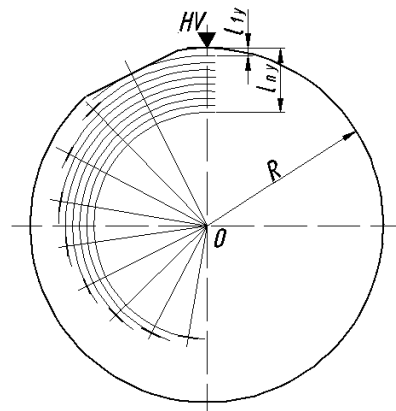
Схема розташування мікрошліфів на сферичній поверхні
